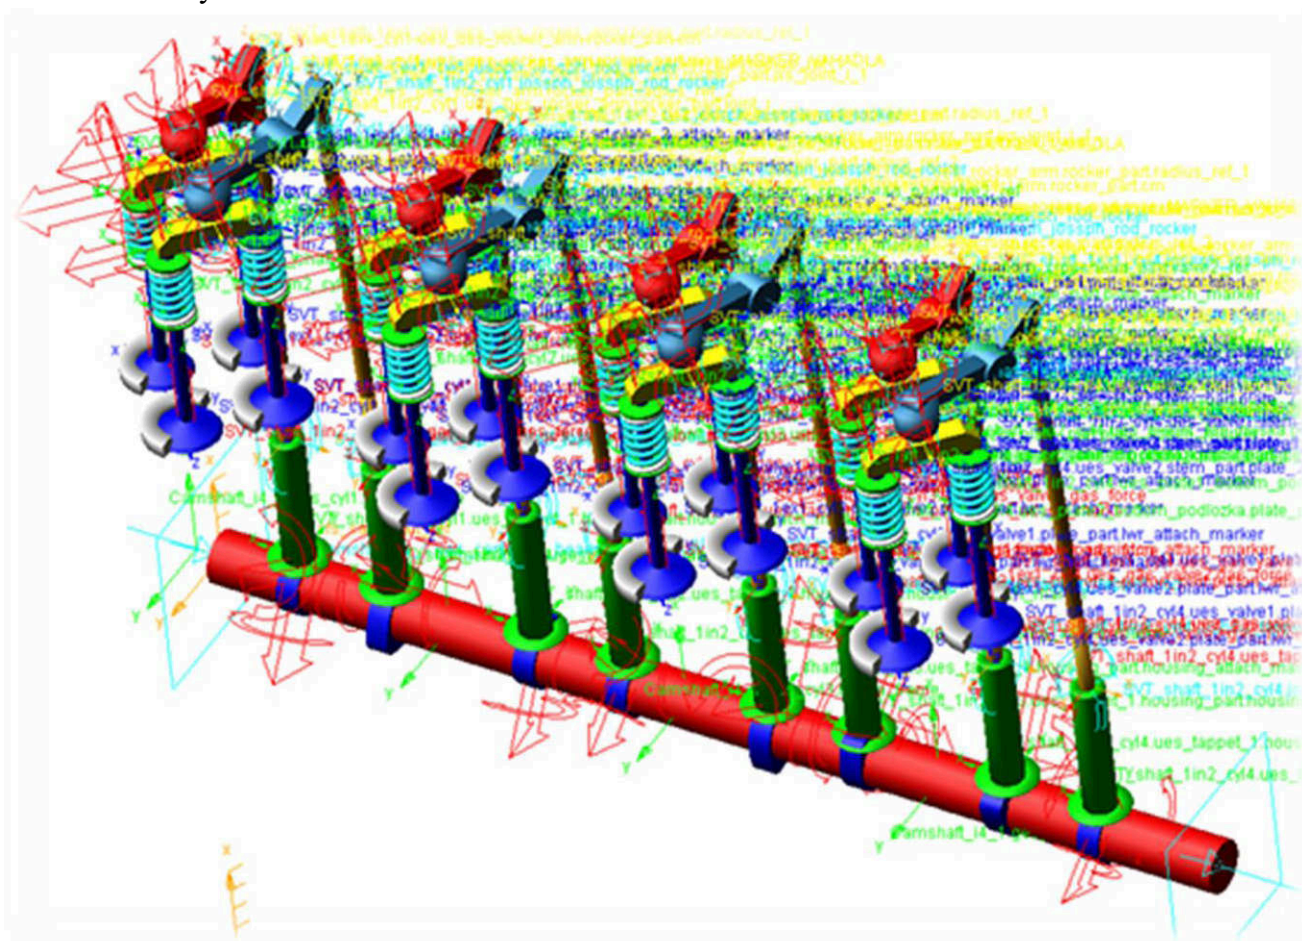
Pohled zezadu a z boku na ventilový OHV rozvod čtyřventilové hlavy motoru pro čtyřválcový motor sestavený v Adams/Engine
